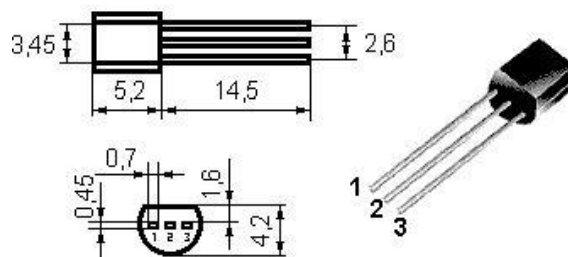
Габаритні розміри мікросхеми 78L09
